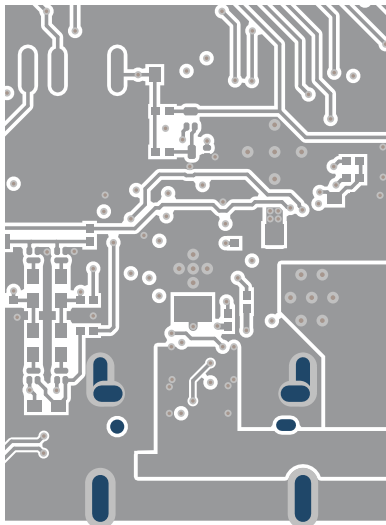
TPS26750 PCB Layout - Bottom Layer 6
